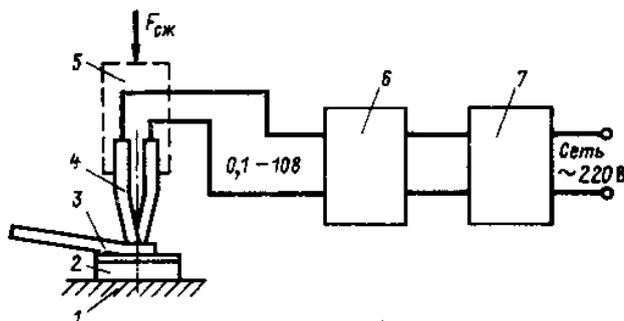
Схема сварки давлением с косвенным нагревом:
